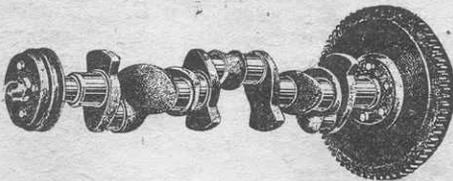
Коленчатый вал шестицилиндрового двигателя автомобиля Оклад.
